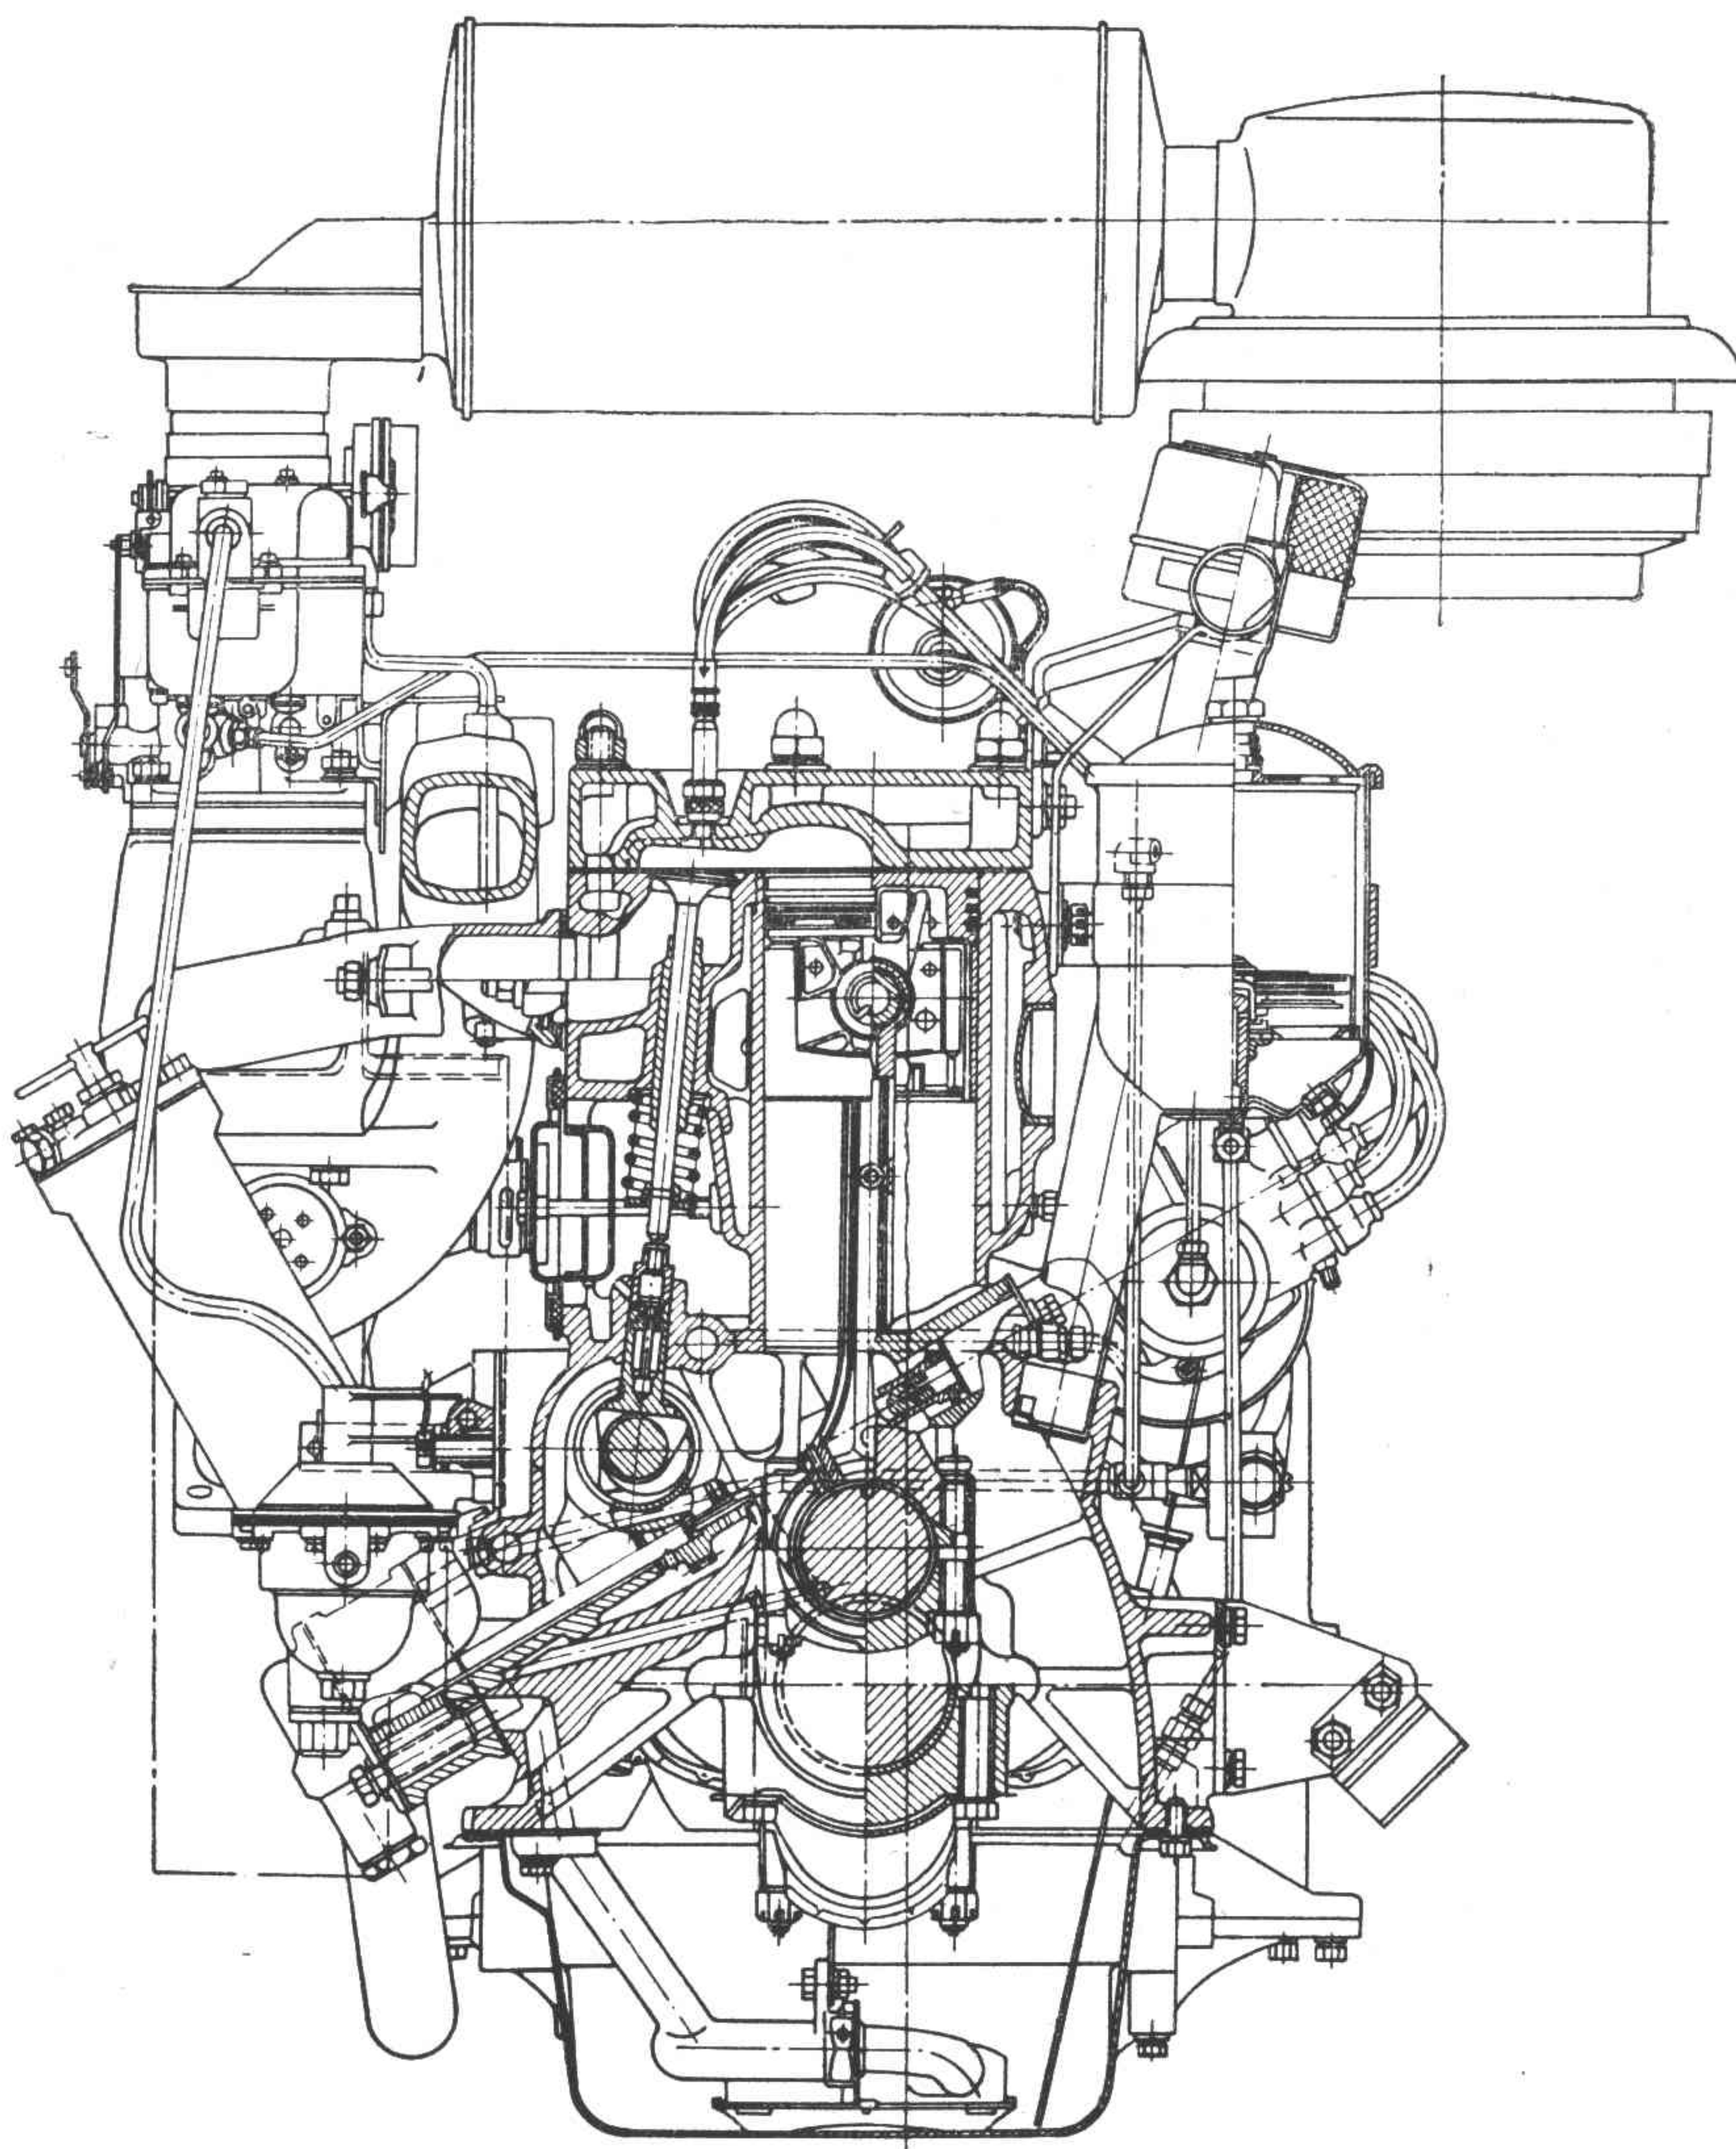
Поперечный разрез двигателя ЗИЛ-110
